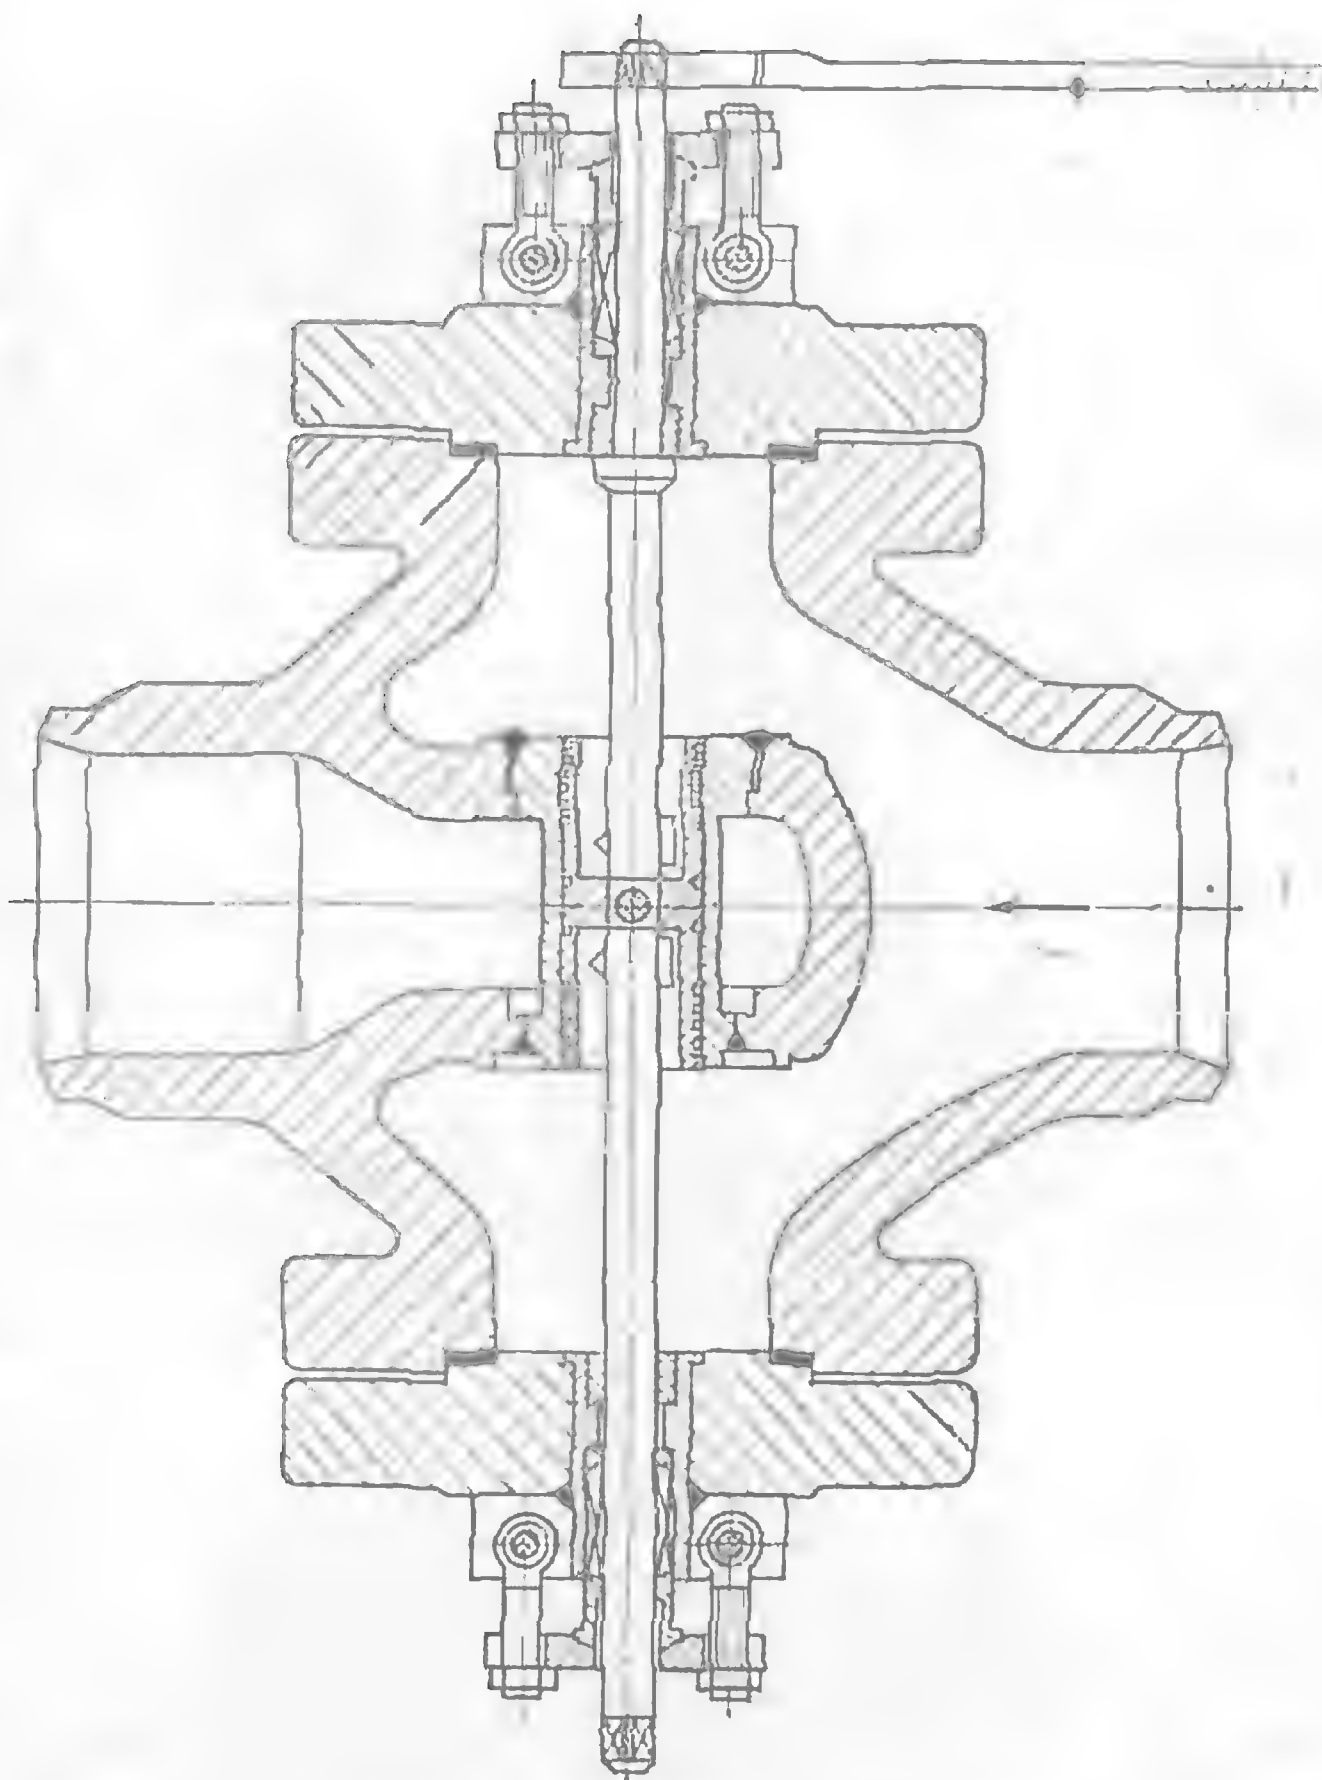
Регулирующий питательный клапан поворотного типа с цилиндрическим золотником.
